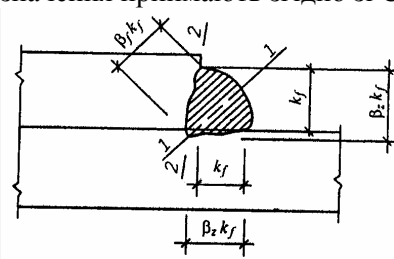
Розрахункова схема кутового шва: 1, 2 – розрахункові перерізи за наплавленим металом та межею сплавлення
